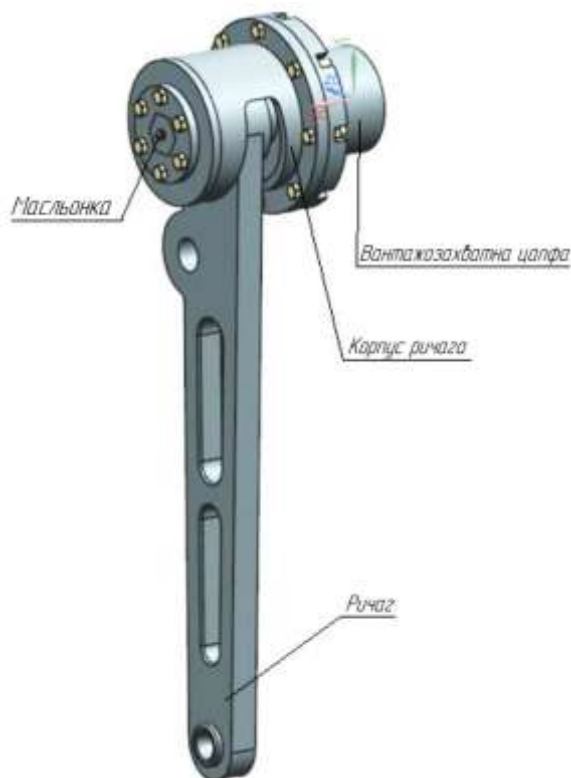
Загальний вигляд важеля і корпусу МВДК
